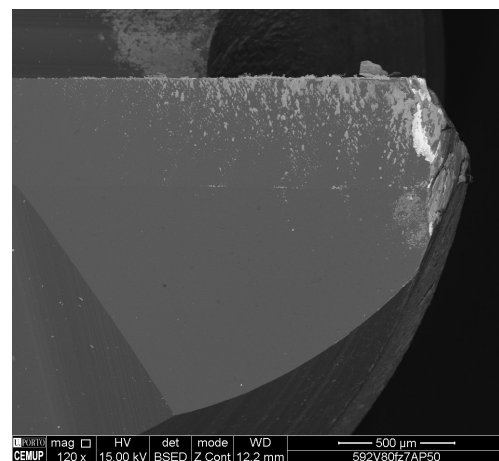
Fissuração presente no teste V1F3A1 da ferramenta 592.
